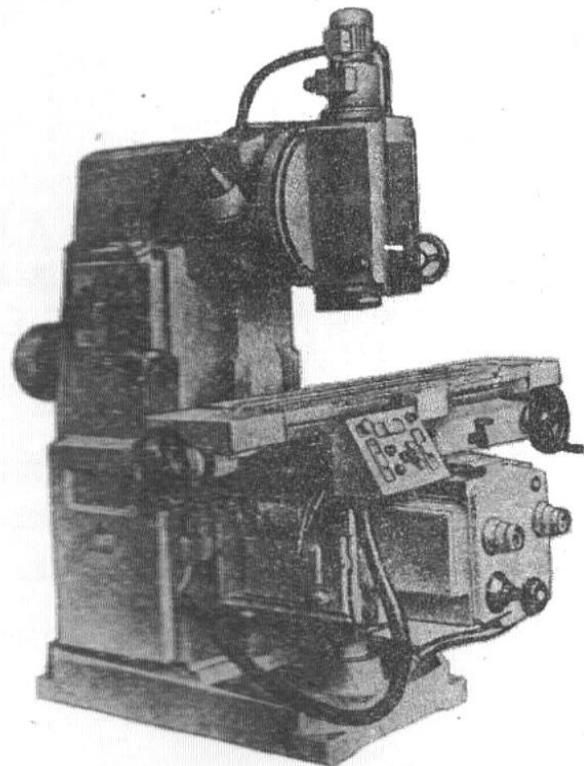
Вертикальный консольно-фрезерный станок 6Т13
